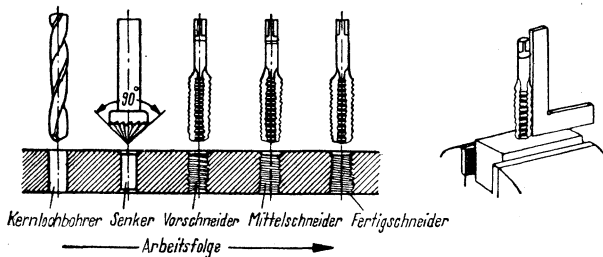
Arbeitsfolge beim Gewindebohren (links) und Kontrolle des richtigen Ansatzes mit dem Winkel (rechts)
